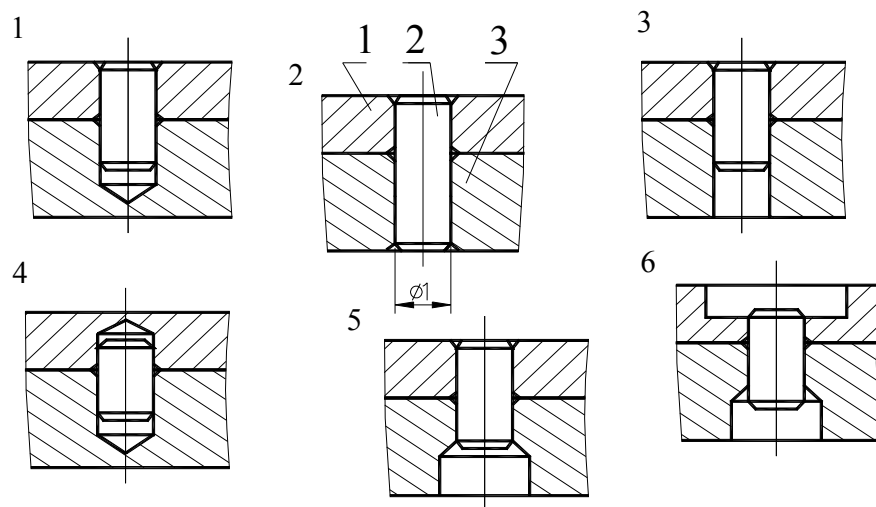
Установочный штифт 2 должен быть неподвижно закреплён в детали 1, а с деталью 3 должен сопрягаться по посадке, близкой к посадке скольжения. Укажите правильный вариант конструкции
